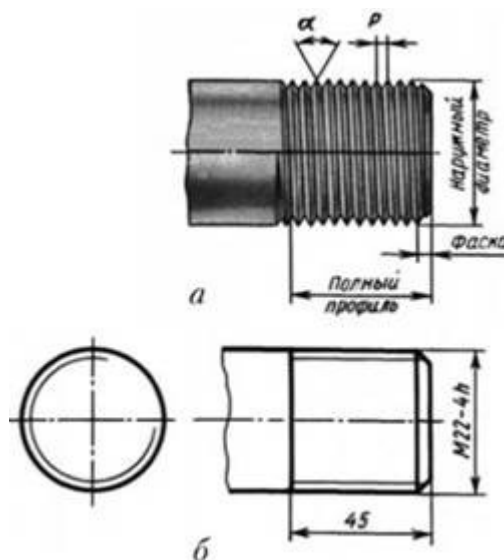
а) Резьба на стержне в реальном виде, б) Резьба на стержне на чертеже.
